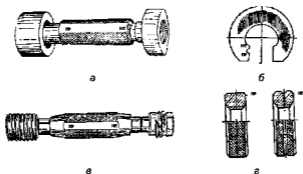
Предельные калибры: *а* – калибр-пробка; *б* – калибр-скоба; *в* – резьбовой калибр-пробка; *z* – резьбовой калибр-скоба
